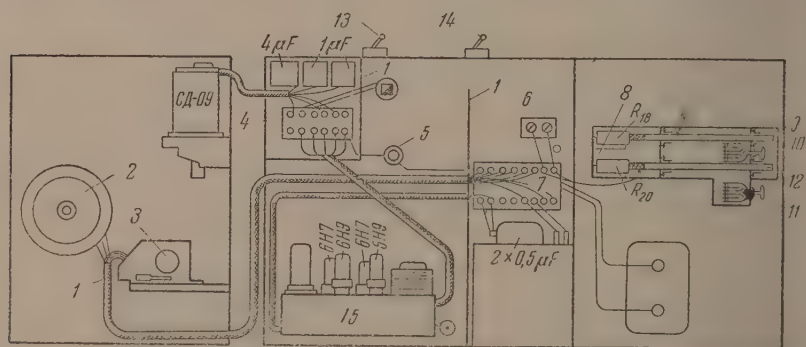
Схема расположения узла. 1—экран; 2—реохорда; 3—механизм установки рабочего тока; 4—колодка № 2; 5—земля; 6—вход; 7—колодка № 1; 8—измерительный мост; 9—установка нуля; 10—переключатель входа; 11—проверка пределов; 12—установка предела; 13—выключение диаграммы; 14—включение прибора, 15—усилитель
